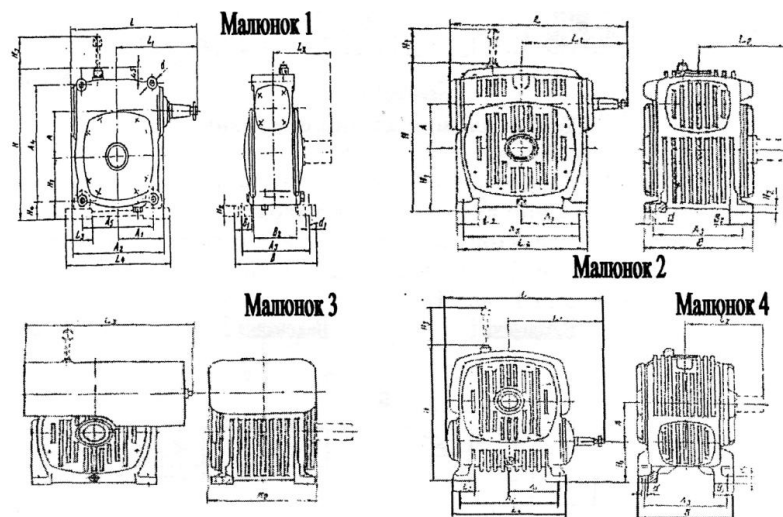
Редуктор РГВ. Рис. 2. Редуктор РГУ. Рис. 4. Редуктор РГВВ. Рис 5. Редуктор РГН.
